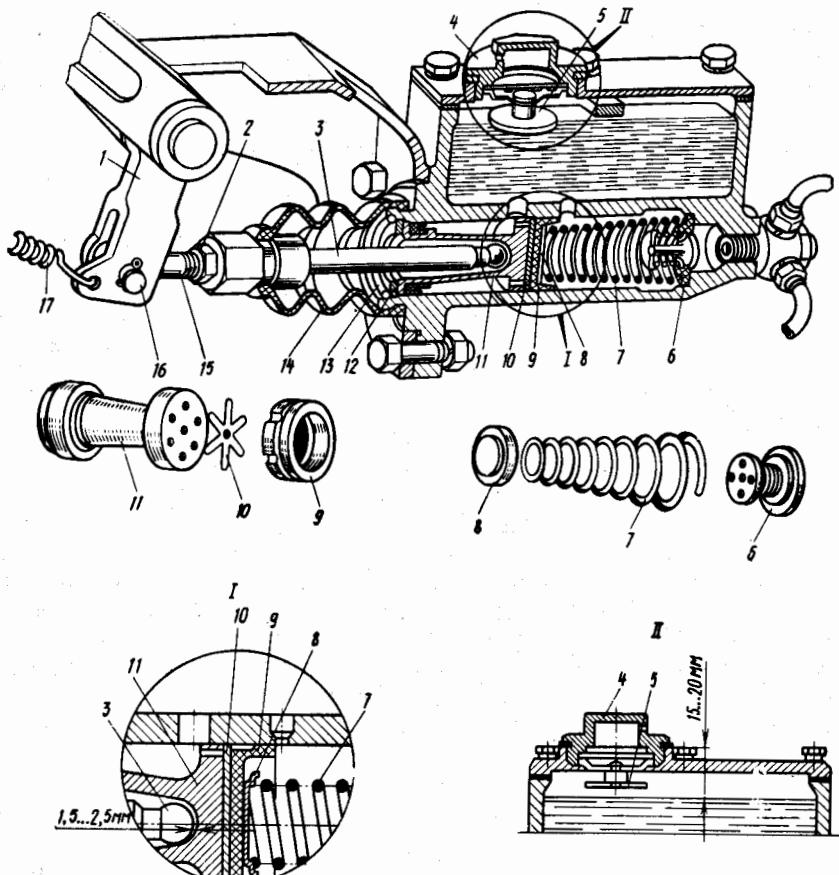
Главный цилиндр гидравлического привода автомобиля ГАЗ-53-12:
